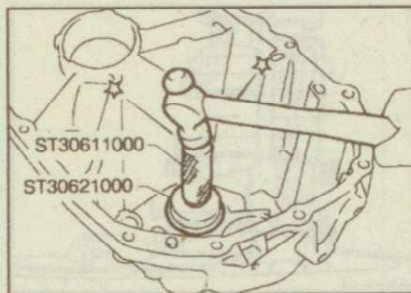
Установка наружного кольца подшипника вторичного вала
